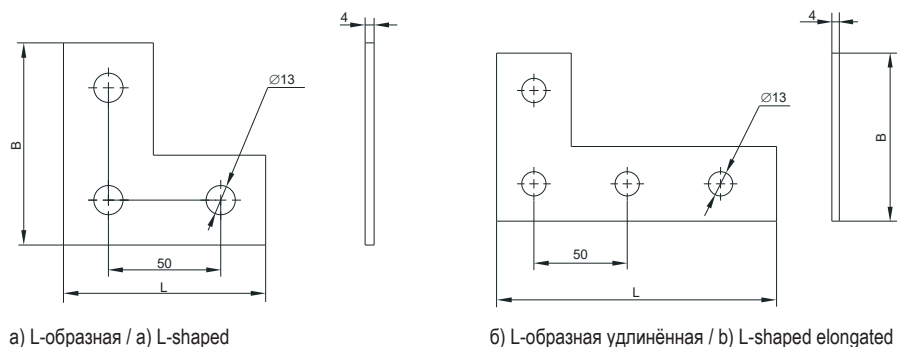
Пластина соединительная L-образная для STRUT-профиля / Figure I.2 – L-shaped joining plate for STRUT profile
